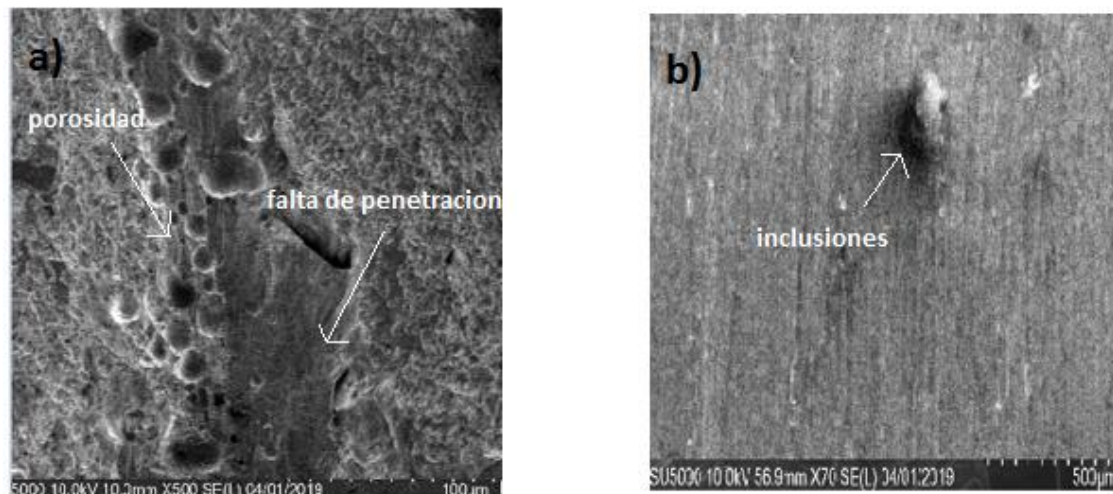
Defectos en soldadura (a) (356 J/mm) (b) (373 J/mm).
